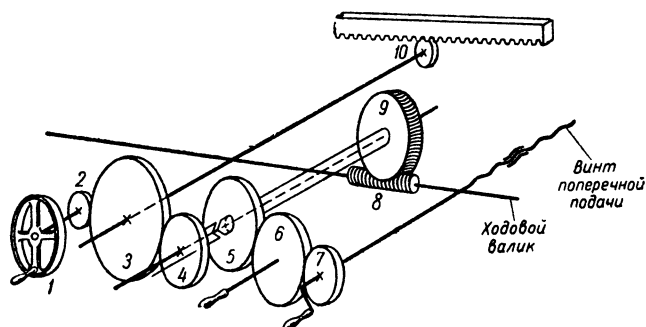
Кинематическая схема фартука токарно-винторезного станка 1615-М.
